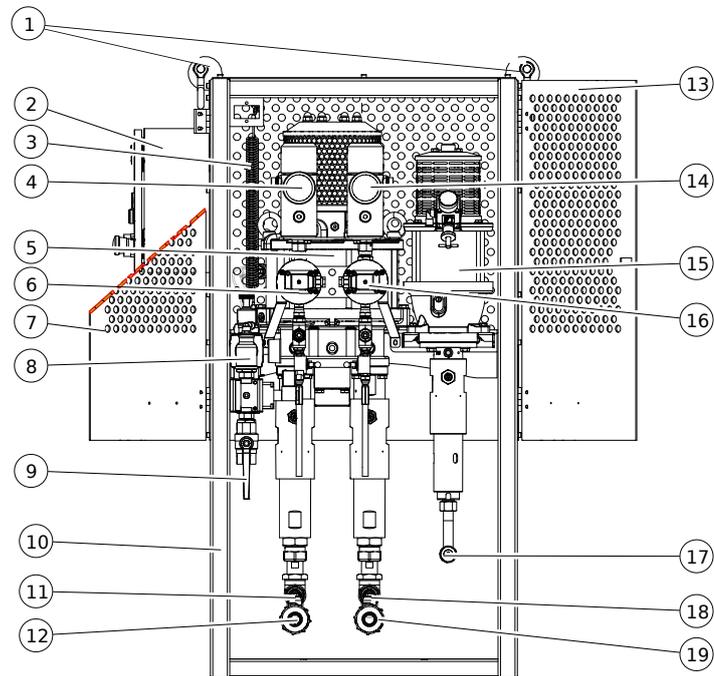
Aufbau Inject 230 mit Steuerschrank
